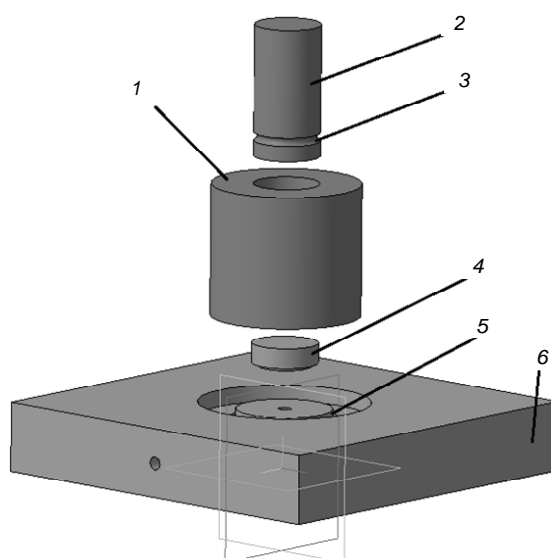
3D-изображение пресс-формы для получения дисковых заготовок:
